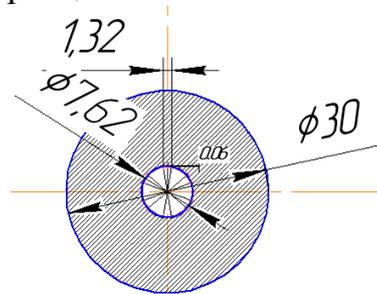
Поперечное сечения ствола винтовки образца 1891/30г. с полигональным профилем
